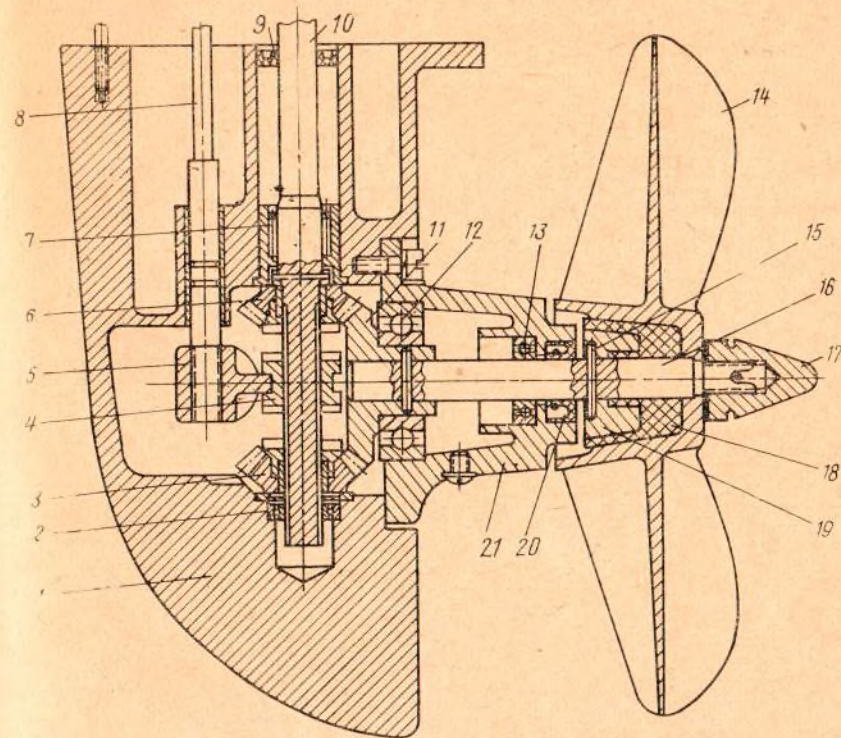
Реверс-редуктор подвешного мотора «Москва»
